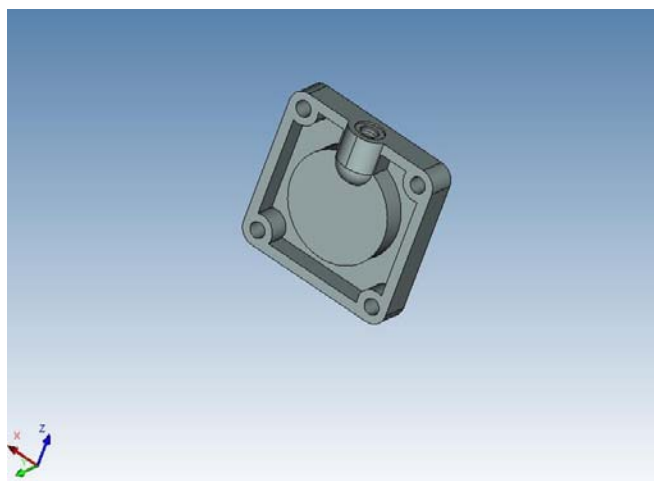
3D модель крышки задней двухстороннего пневматического цилиндра
